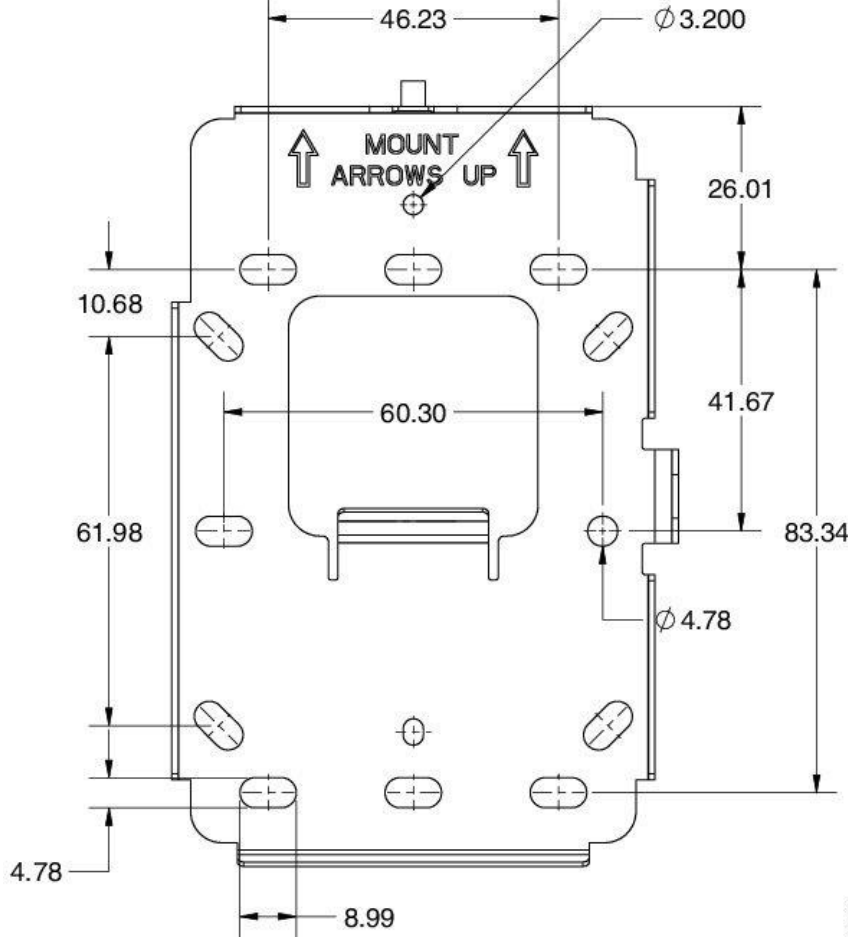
Duvara Montaj Braketi AIR-AP-BRACKET-W3
